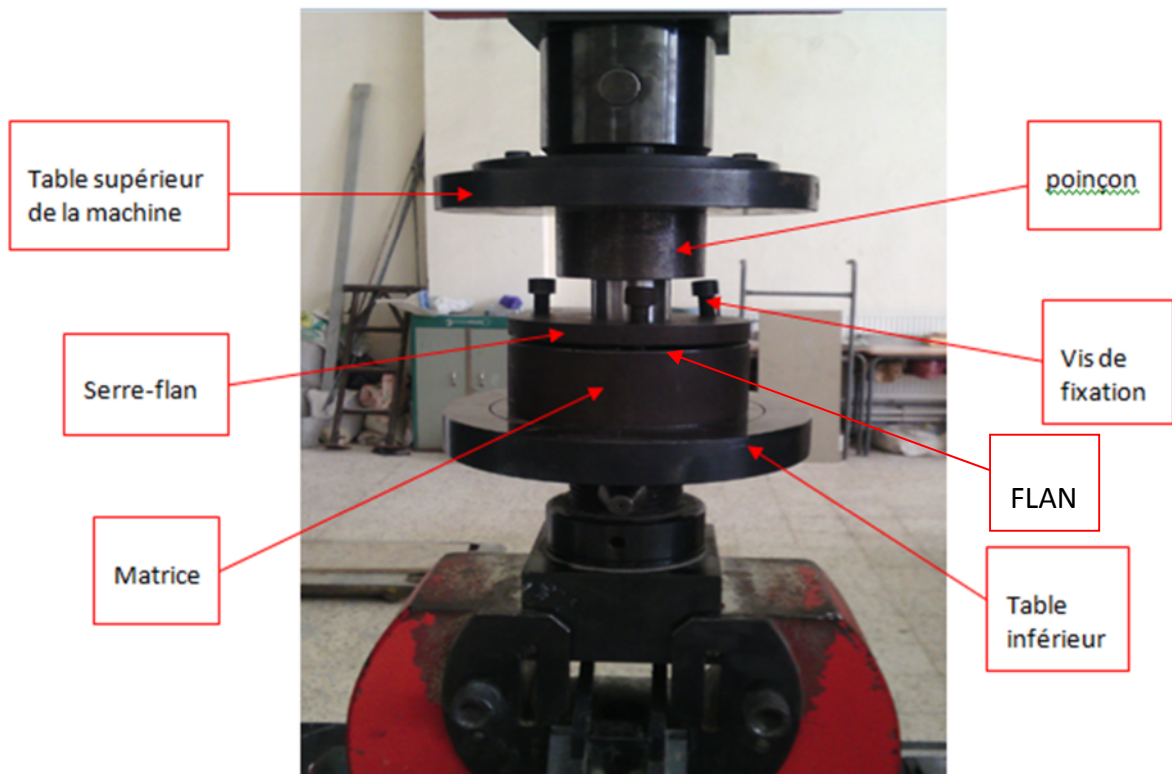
Montage de l'outil d'emboutissage sur la machine
